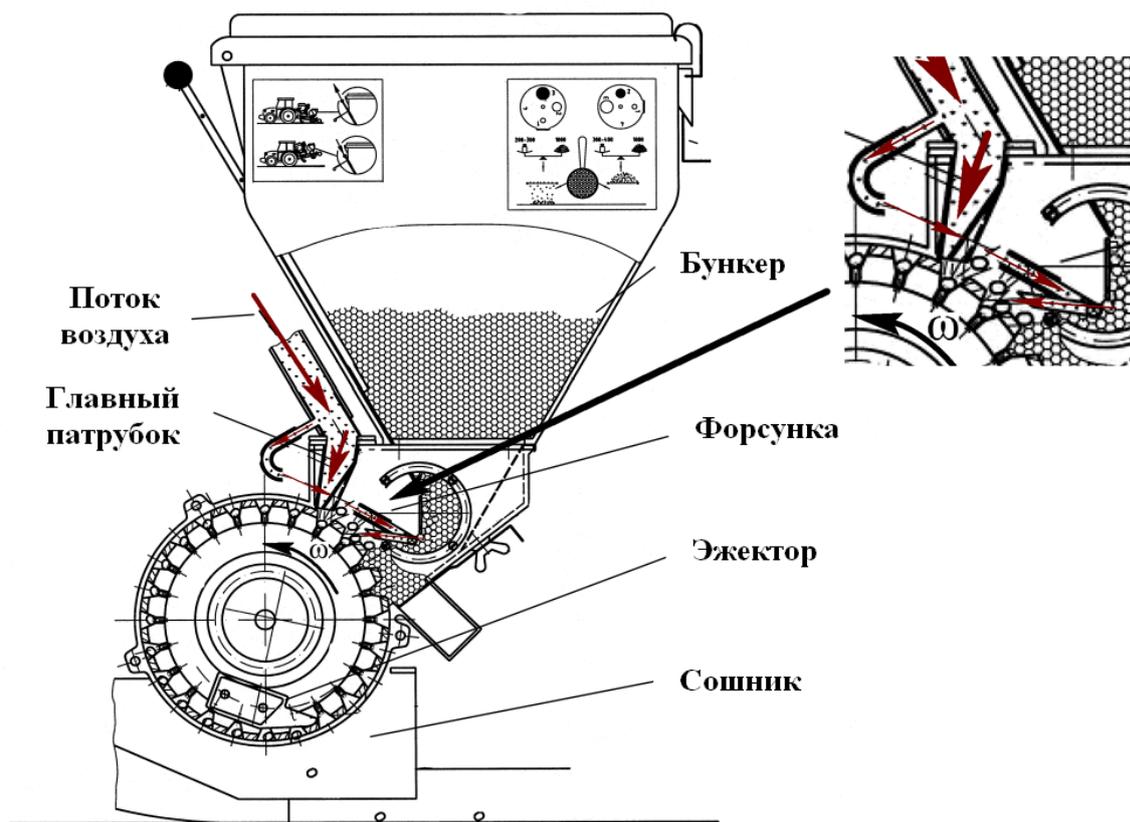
Схема работы высевающего аппарата избыточного давления.
